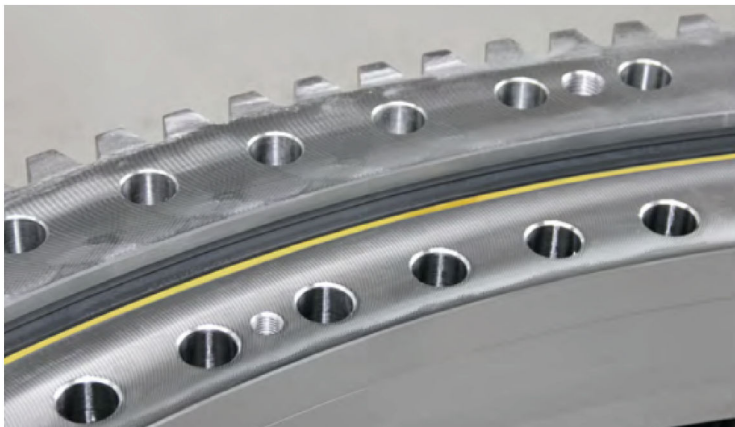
Geschlossener Fettkragen an Lagerdichtung
